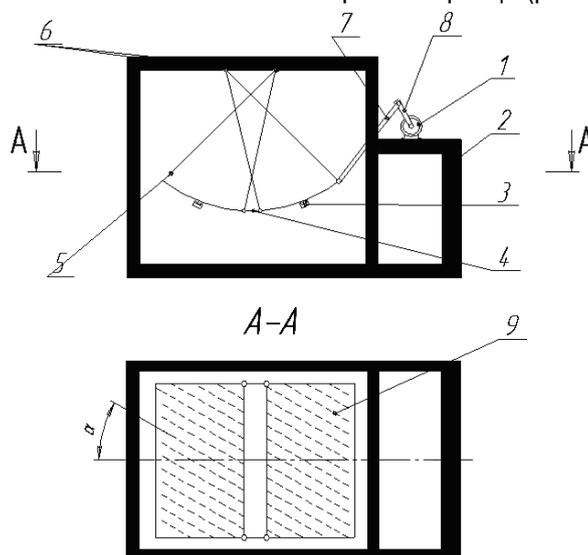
Схема лабораторного образца машины для сепарации зернового вороха с качающимися рабочими органами:
